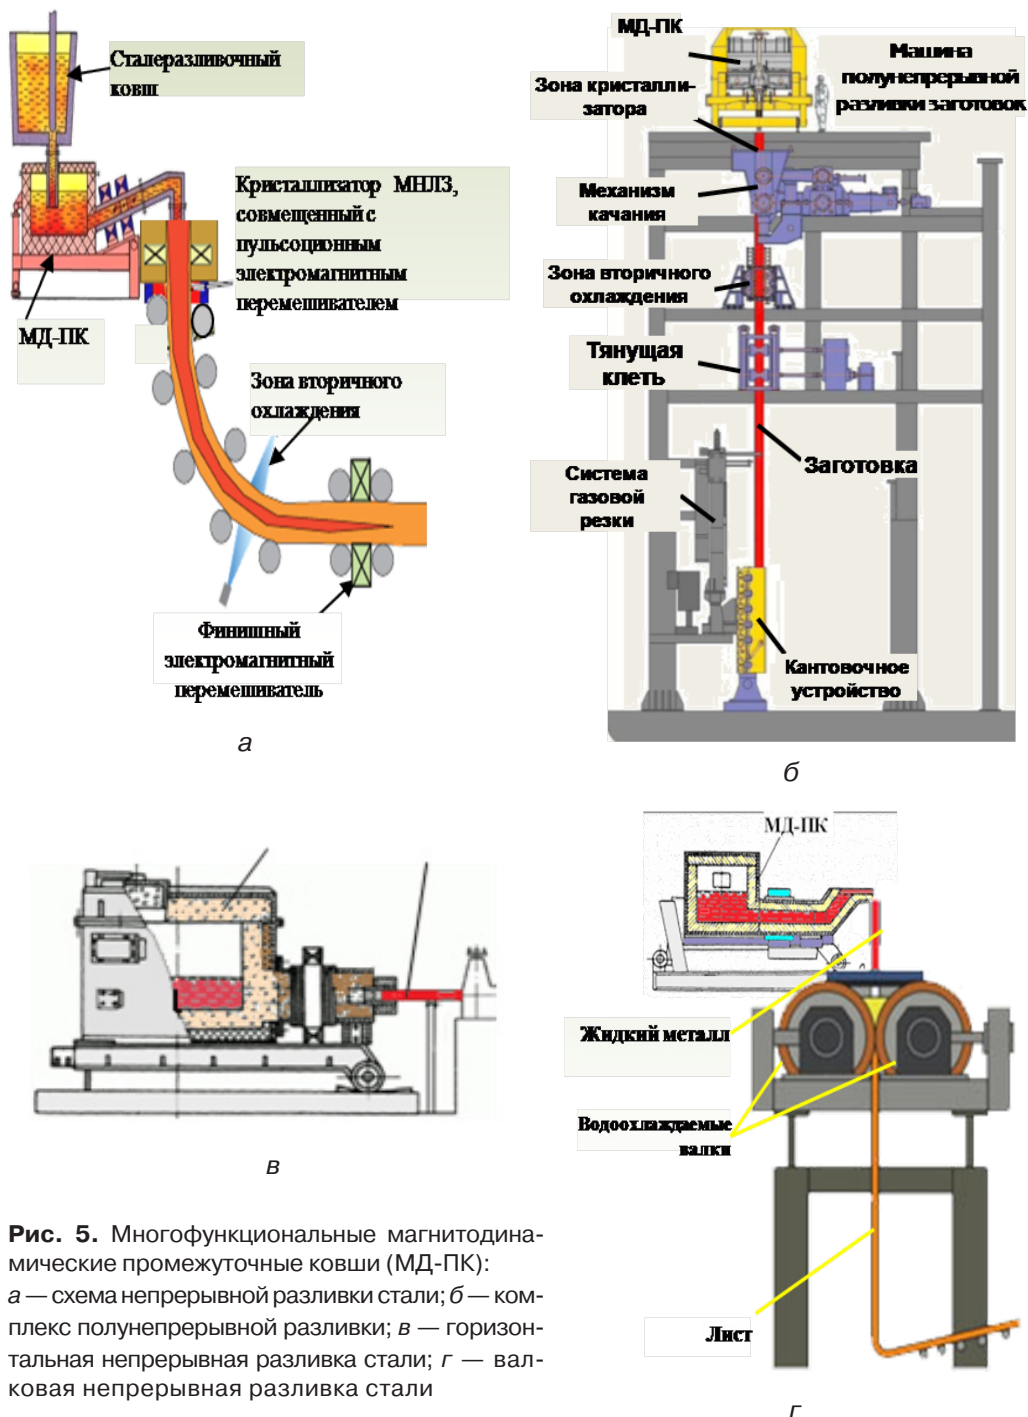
Многофункциональные магнитодинамические промежуточные ковши (МД-ПК): а — схема непрерывной разливки стали; б — комплекс полунепрерывной разливки; в — горизонтальная непрерывная разливка стали; г — валковая непрерывная разливка стали
